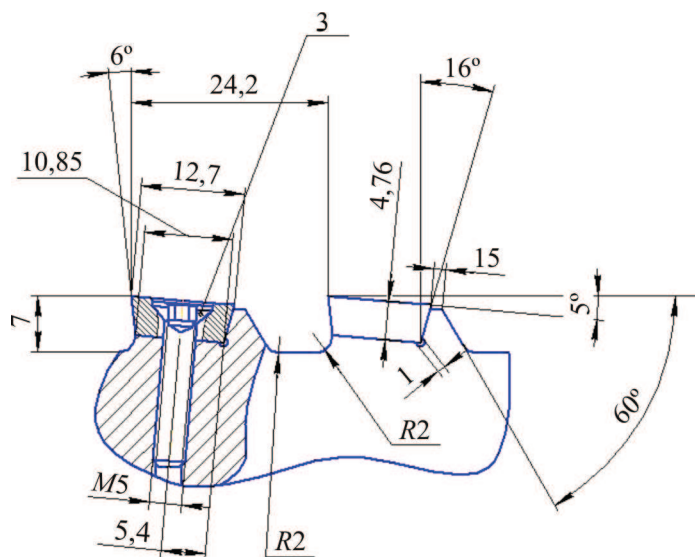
Схема крепления многогранной сменной пластинки на корпусе протяжки
